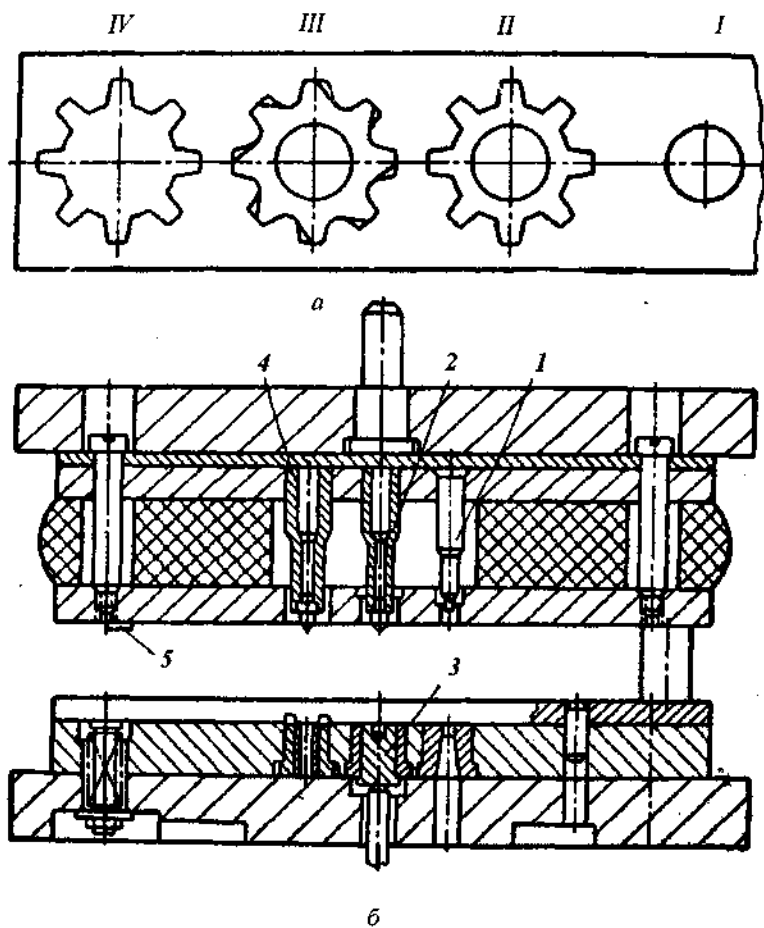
Штамп последовательного действия с запрессовкой заготовки в полосу:
